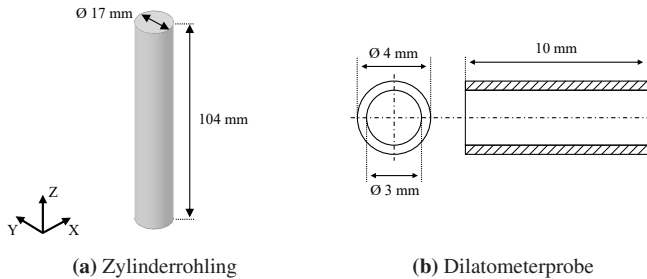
Darstellung des (a) mittels PBF-LB gefertigten Zylinderrohling (S8) für die Herstellung der Dilatometerproben sowie (b) finale Hohlprobengeometrie nach der subtraktiven Bearbeitung.
